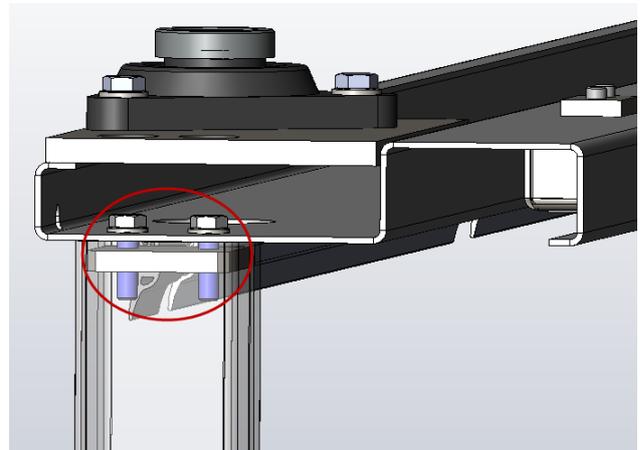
Verschweißen der Winkelzarge
